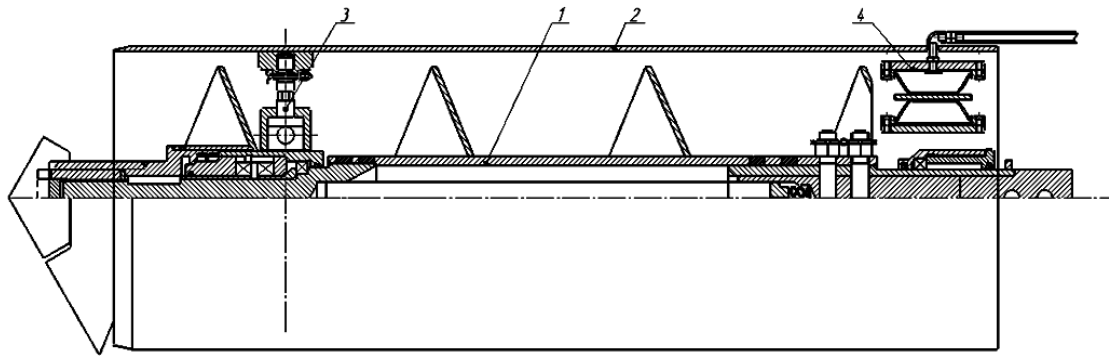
Устройство корректировки траектории: 1 – вал; 2 – корпус трубы; 3 – передняя подвеска; 4 – задняя подвеска
